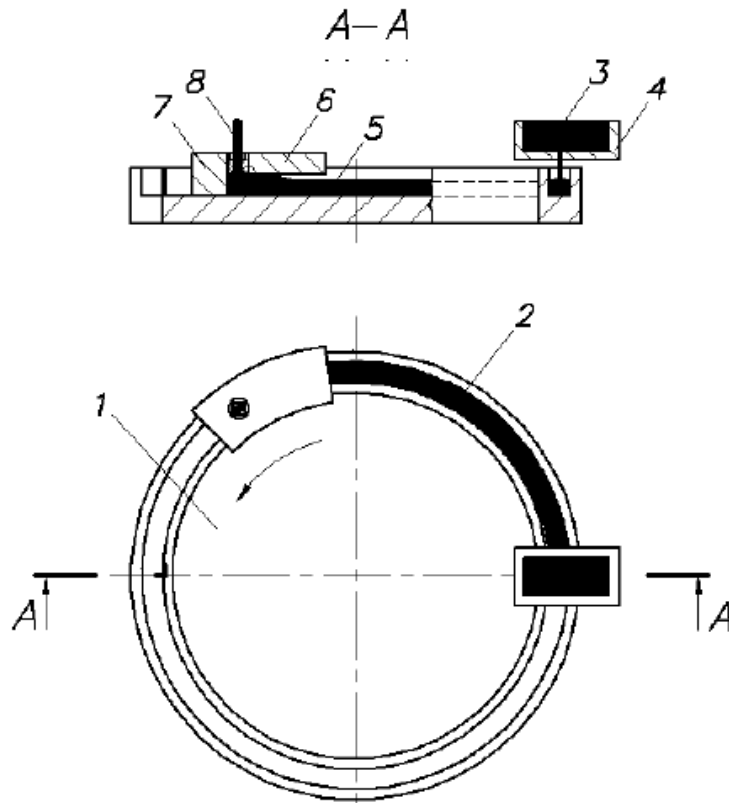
Схема установки непрерывного литья - прессования с вертикальной осью вращения колеса: 1 - колесо-кристаллизатор; 2 – ручей; 3 – жидкий металл; 4 – литниковая коробка; 5 – слиток; 6 – матрицедержатель; 7 – матрица; 8 – пресс-изделие
